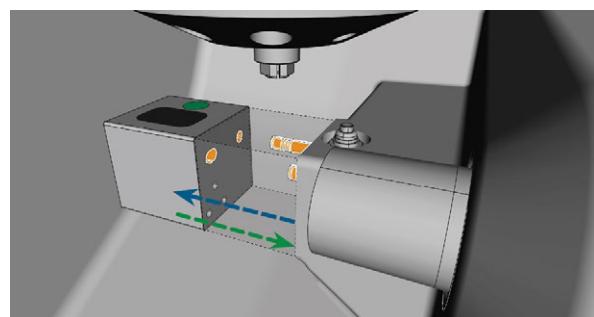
REMPLACER LE MAGASIN D'OUTILS (SUPPORT DU MAGASIN D'OUTILS ET TROUS DANS LE MAGASIN D'OUTILS MARQUÉS EN ORANGE)
